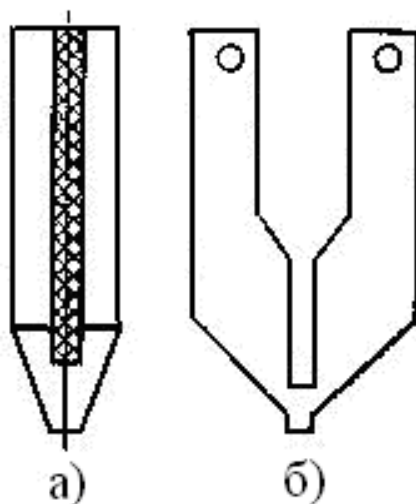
V-образный инструмент для сварки с косвенным импульсным нагревом:
